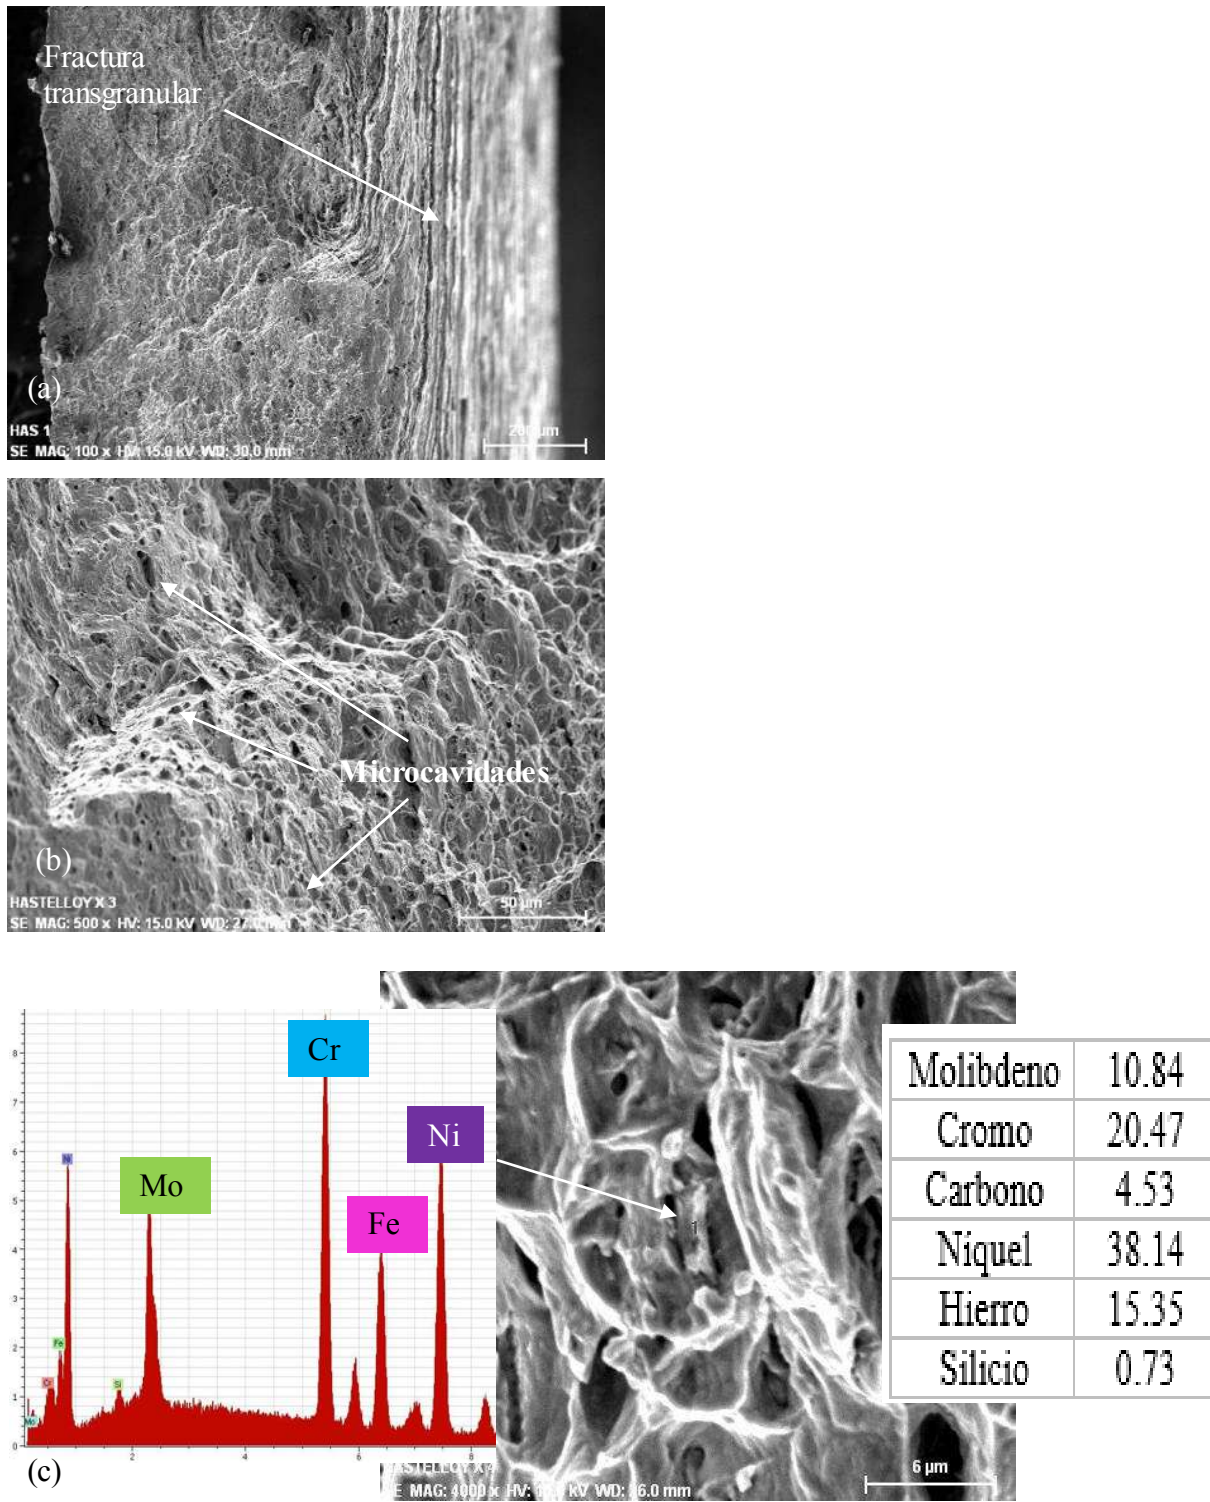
Análisis de la fractura mediante MEB en las probetas sometidas a tensión de la unión soldada tipo A.
